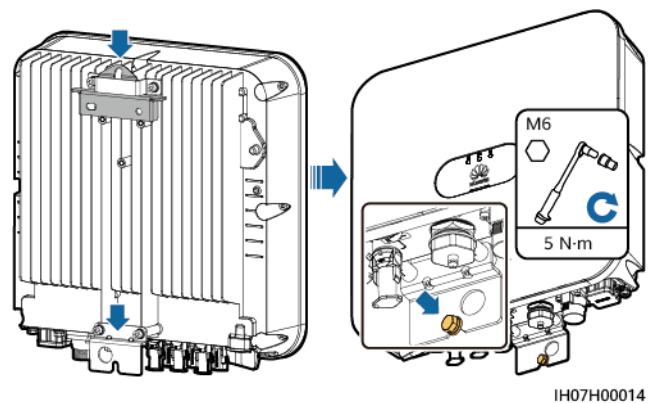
Instalação de um parafuso de travamento na DC switch
